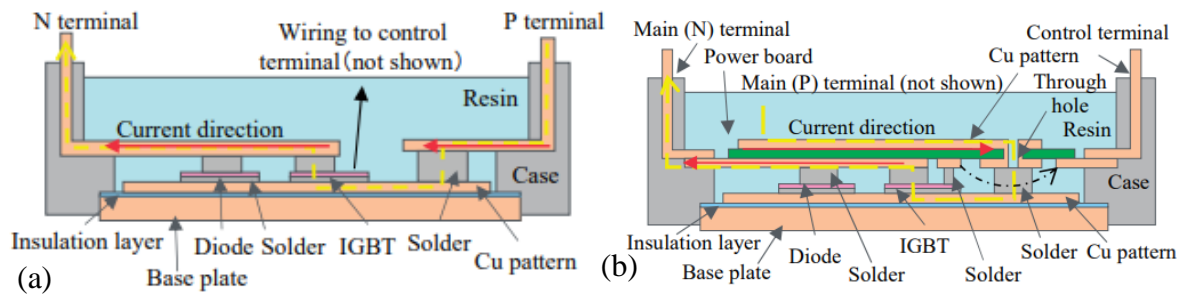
Vue en coupe du module (a) DLB .Ref [65] (b) DLB développé [61]
